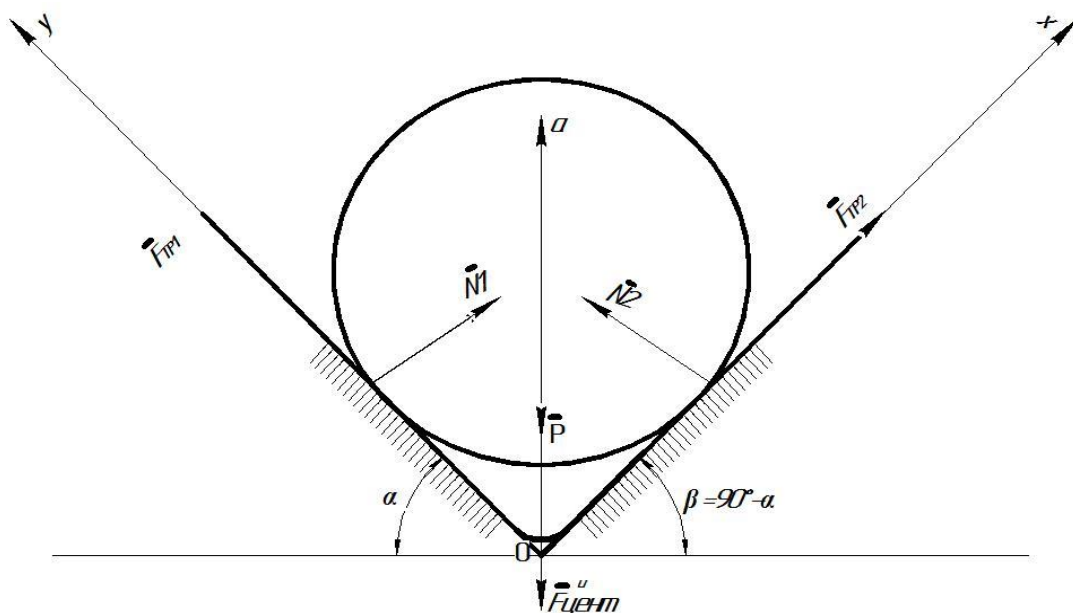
Схема обработка шаровидной заготовки в канавке галтовочного станка с горизонтальной осью вращения
